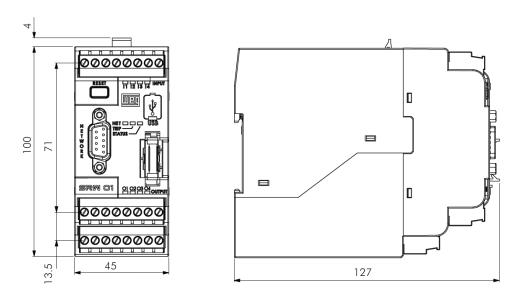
Dimensiones de la Unidad de Control – UC (mm)
